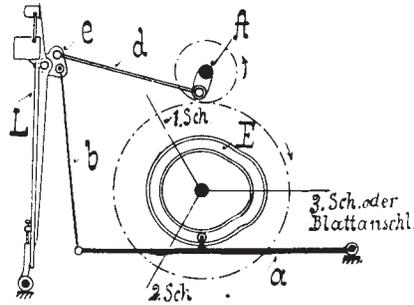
Ladenbewegung mit zwei Anschlagstellungen.
